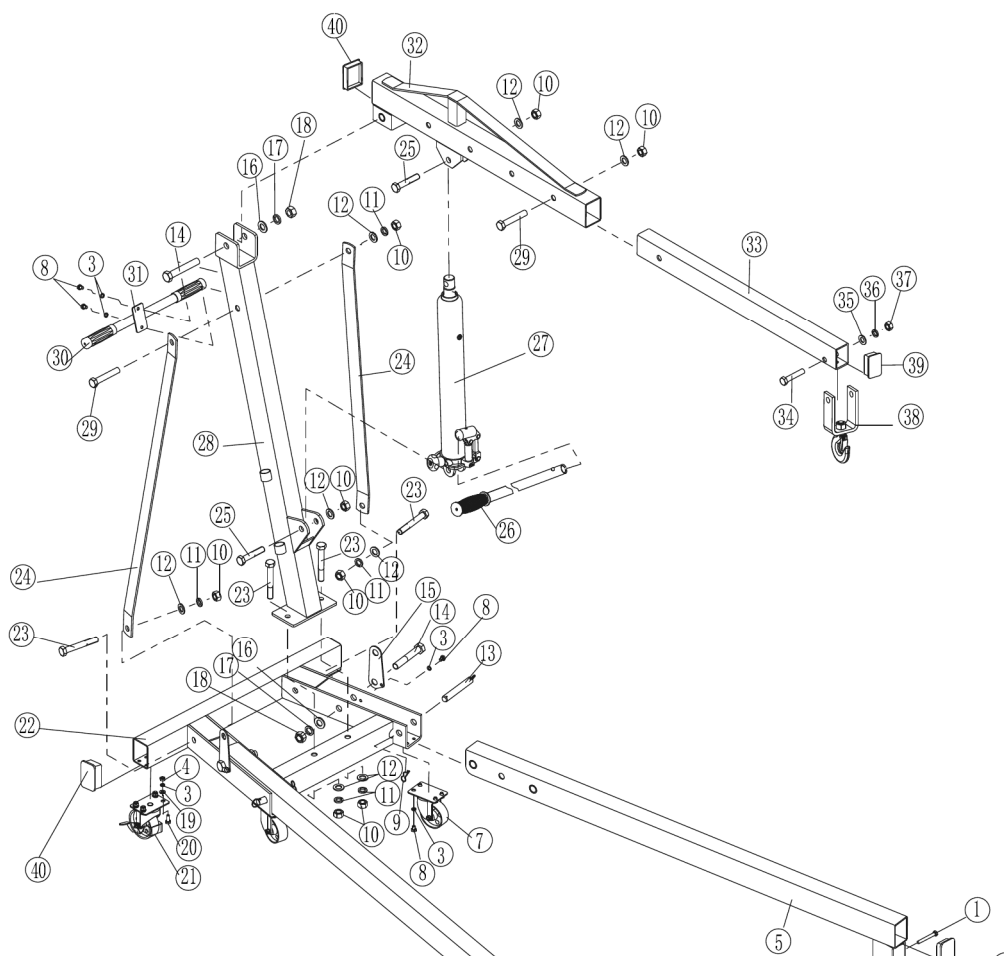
Vista explodida do AY 1 TN GR (588590)
